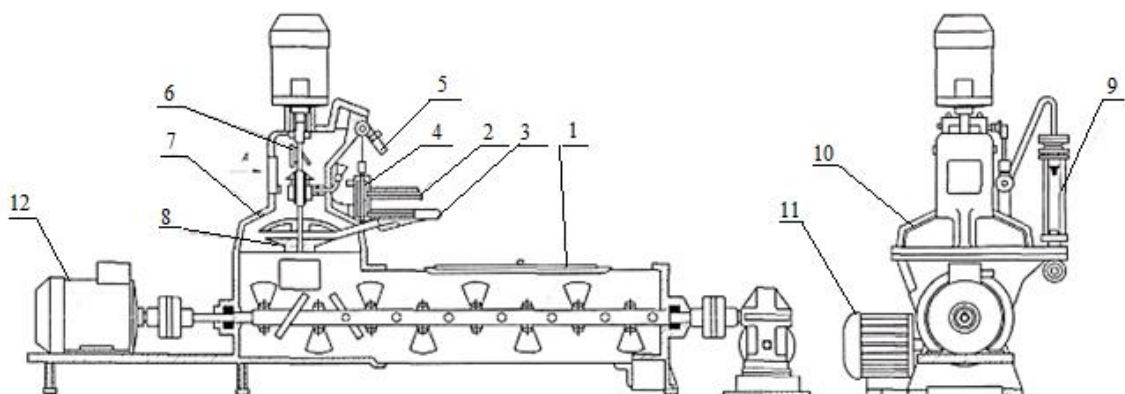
Зволожувальна машина ЗУМ-2: 1 – шнек-змішувач; 2 – трубка; 3- пристрій для подачі води; 4 – механізм для регулювання подачі води; 5 – важіль з вантажем; 6 – клапан для регулювання подачі зерна; 7 – верхній диск; 8 – нижній диск; 9 – ротаметр; 10 – корпус; 11 і 12 – електричні двигуни
